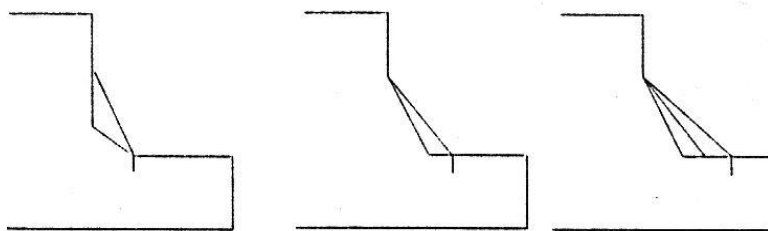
多次焊补焊缝位置、形状示意图
